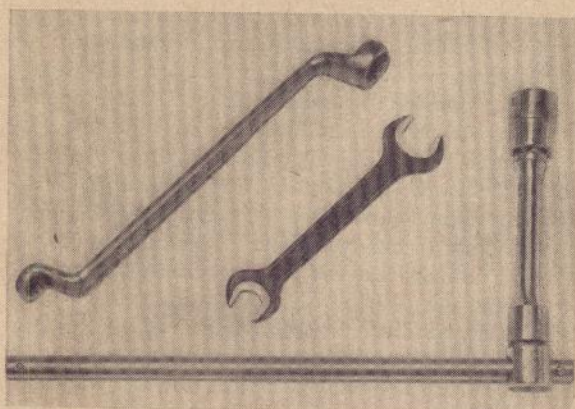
Gekröpfter Ringschlüssel (links), Gabelschlüssel (Mitte) und Steckschlüssel (rechts)
